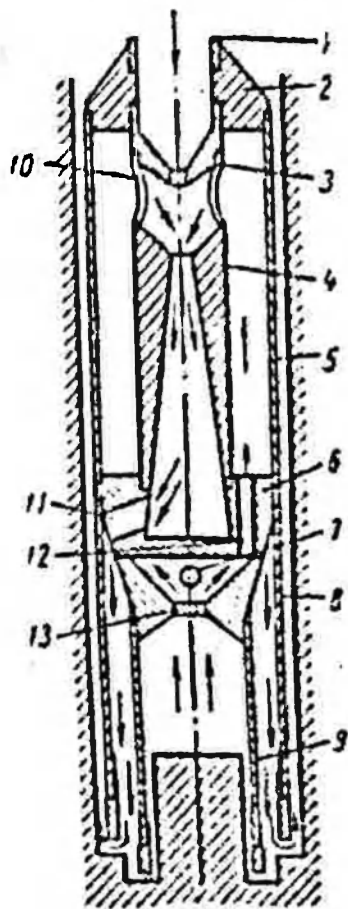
Схема устройства двойного колонкового снаряда конструкции СГП
